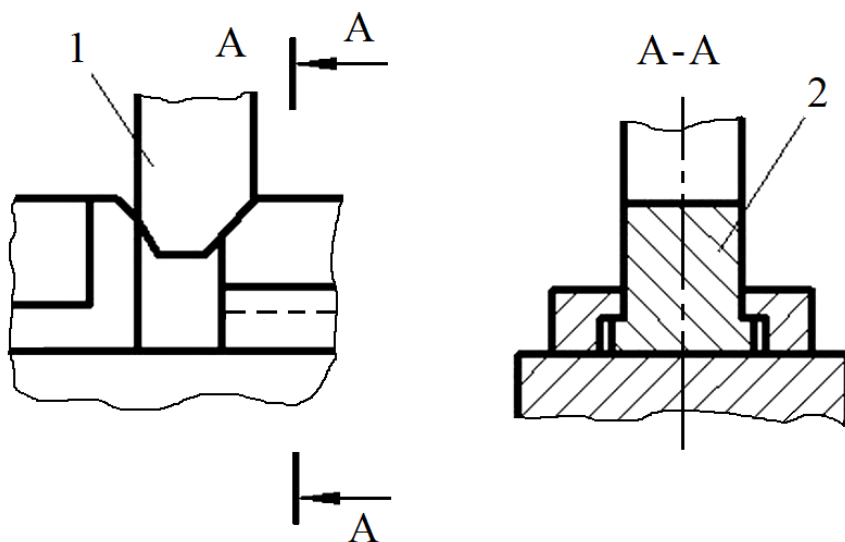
Загальний вигляд клина і повзуна штампа:
